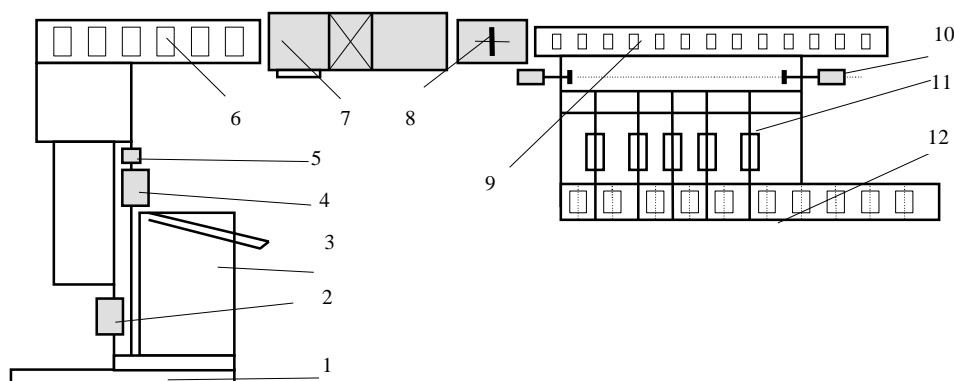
Линия склеивания пиломатериалов по длине ЦНИИМОД-69: 1 - механизм загрузки, 2 - первый шипорезный агрегат, 3 - шина продольного перемещения заготовки, 4 - второй шипорезный агрегат, 5 - клеенаноситель, 6 - питатель, 7 - механизм сборки, 8 - торцовочный станок, 9 - приемный стол, 10 - пресс, 11 - механизм раскрытия и укладки заготовок, 12 - конвейер роликовый
